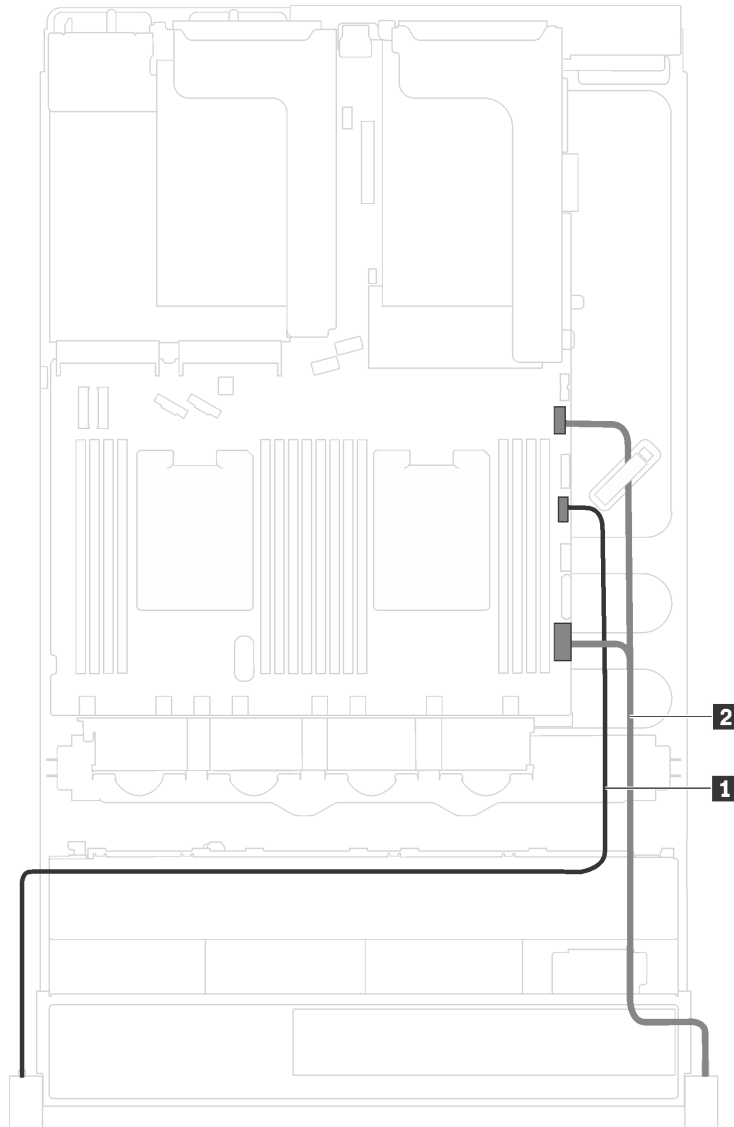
Disposición de los cables del conector VGA y el conjunto de E/S frontal en los pestillos del bastidor
